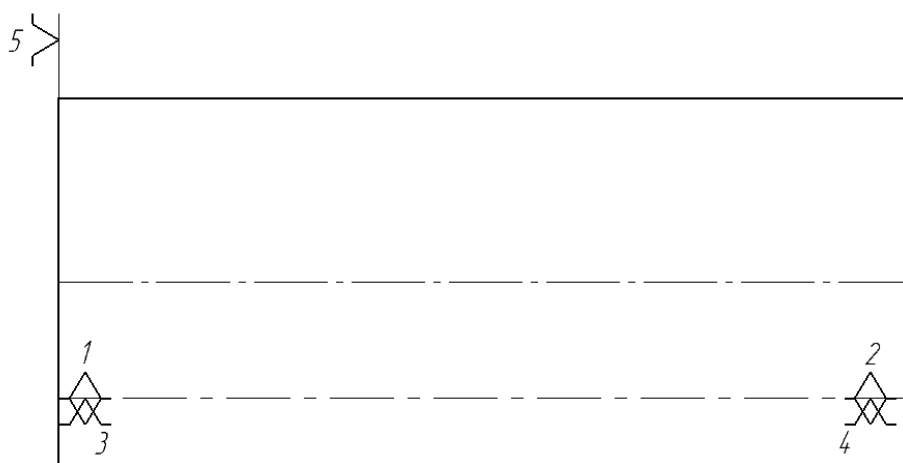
Теоретична схема базування деталі «Вал-шестерня»
